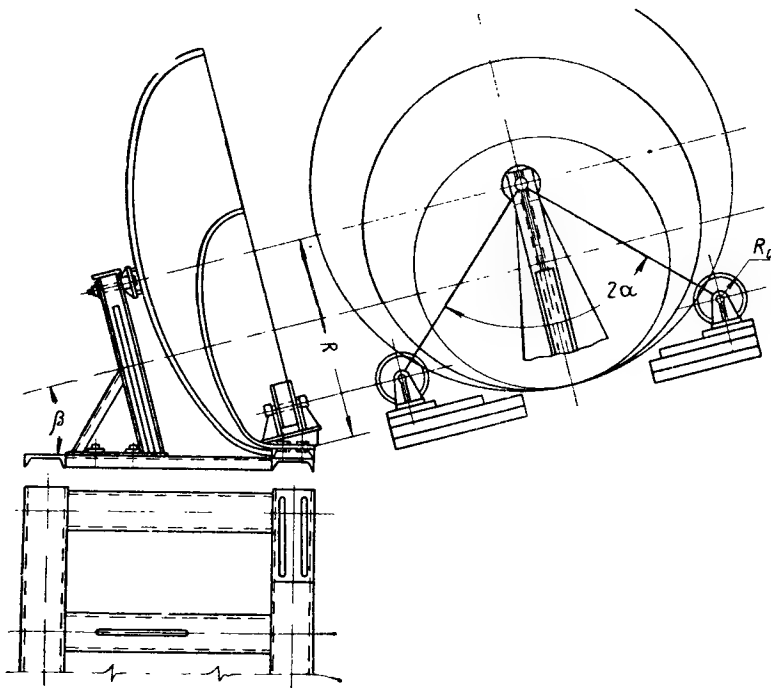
Поворотное приспособление для сварки сферических и эллипсоидальных днищ различных диаметров
